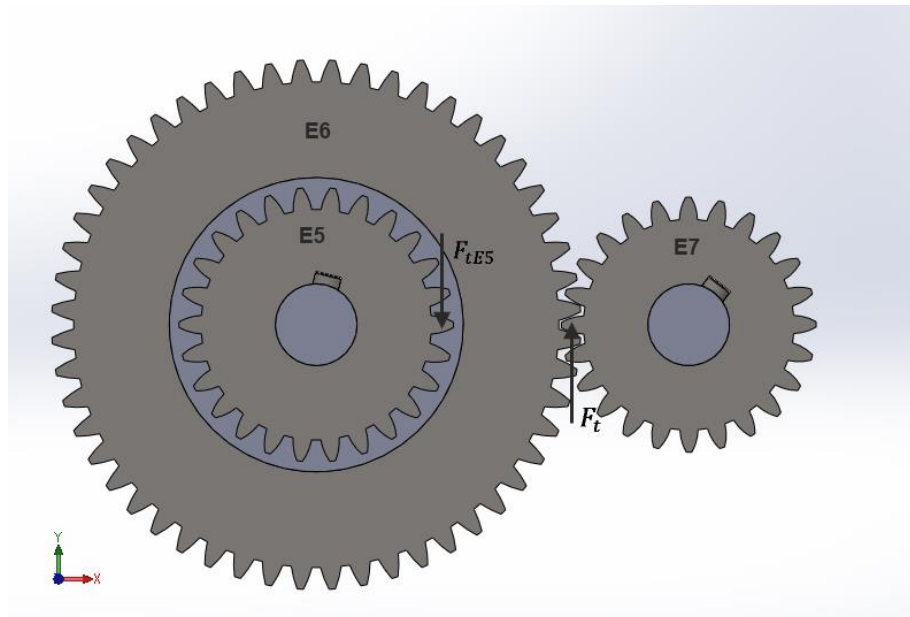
Fuerzas actuantes en el engranaje E5, engranaje E6 y engranaje E7.
